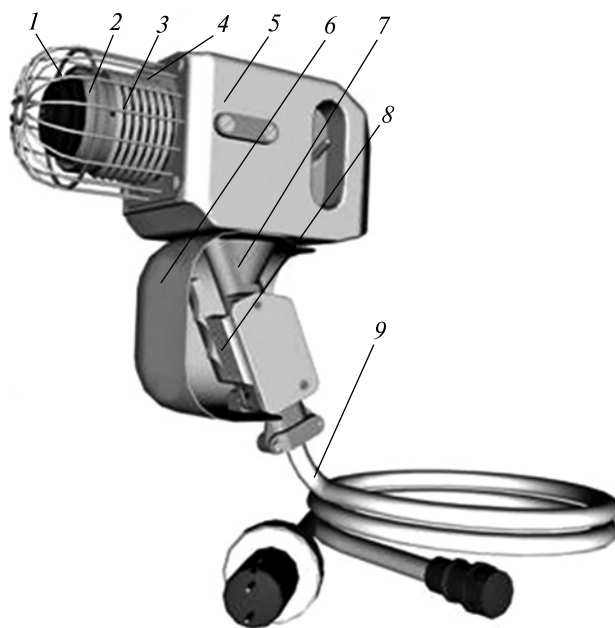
Загальний вигляд ручного електронно-променевого інструмента для зварювання в умовах космосу [12]: 1 — анодний блок, 2 — катодний блок, 3 — радіатор охолодження, 4 — захисна сітка, 5 — корпус катодного блока, 6 — гарда, 7 — рукоятка, 8 — гашетка, 9 — кабель з високовольним з'єднувачем
